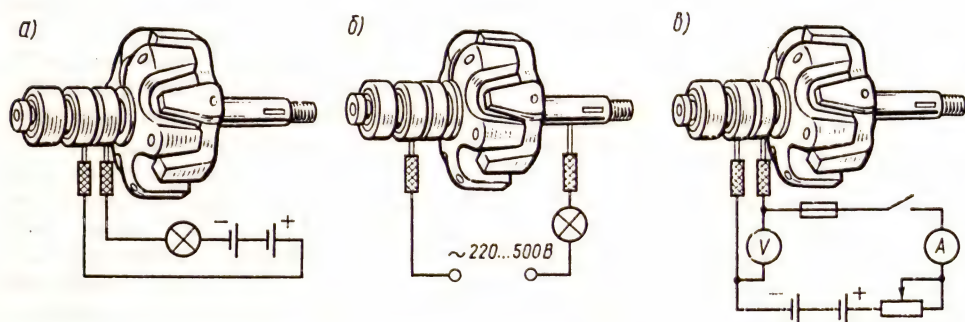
Схемы проверки обмотки возбуждения ротора:
